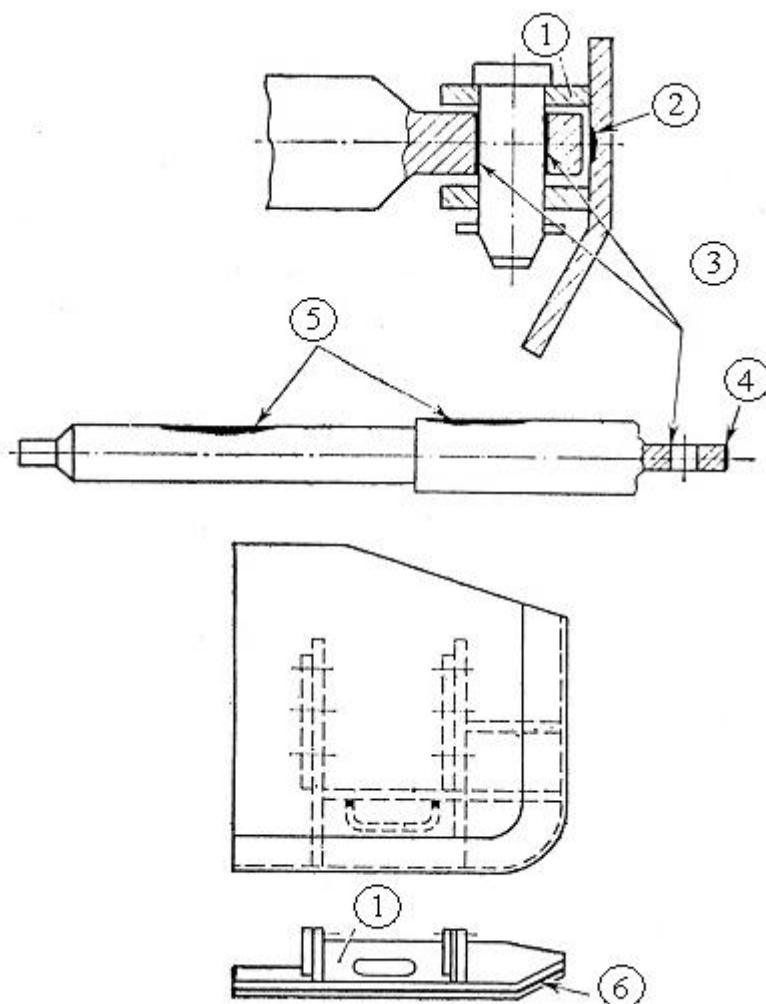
Дефекты деталей безбуферного устройства ЦМВ, ремонтируемые сваркой или наплавкой
